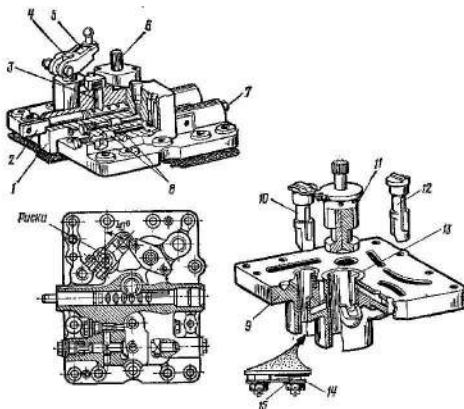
Механизм переключения передач: 1 — крышка; 2 — зубчатая рейка; 3 — фиксатор; 4 и 6 — поводки; 5 — рычаг; 7 — пробка; 8 — перекидные золотники; 9 — корпус; 10 — золотник слива; 11 — золотник переключения передач; 12 — золотник включения механизма отбора мощности; 13 — пилза золотника переключения передач; 14 — защелка; 15 — упор.
